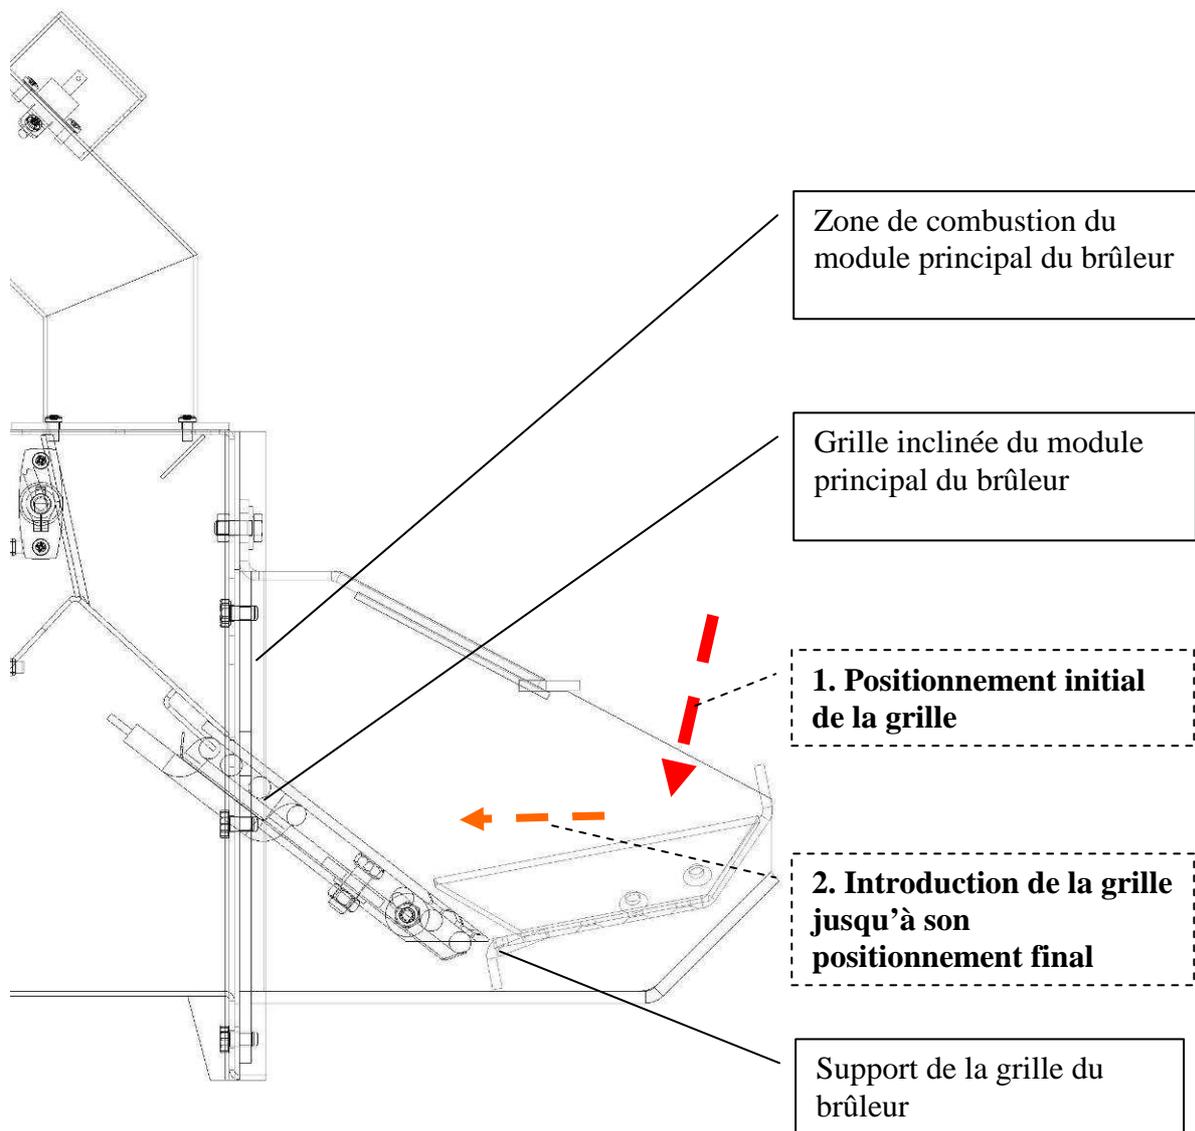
Coupe du module principal du brûleur, démontrant le positionnement de la grille.
